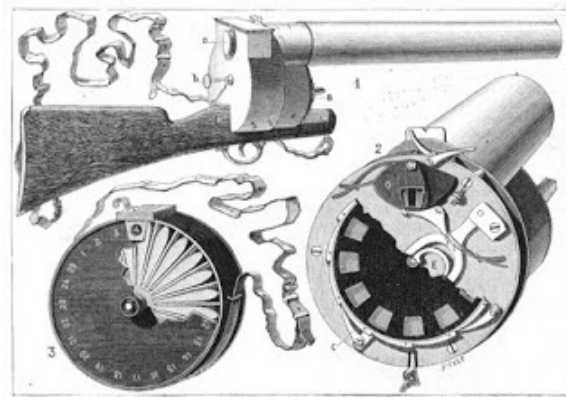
Mécanisme du fusil photographique. — 1. Vue d'ensemble de l'appareil. — 2. Vue de l'obturateur et du disque à soulever. — 3. Boîte contenant vingt-cinq plaques sensibles.
